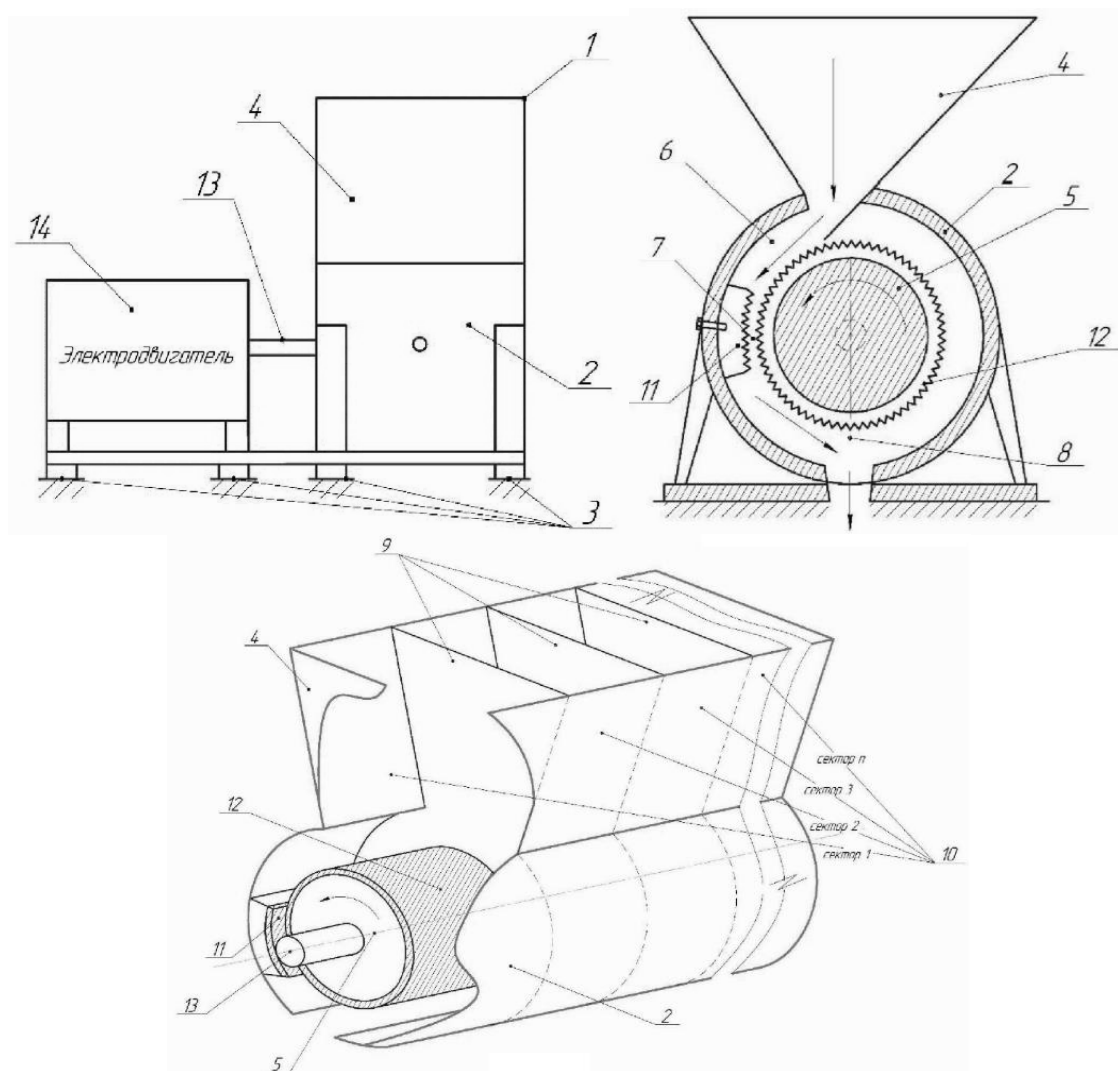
Измельчитель по пат. РФ № 2829351: 1 – измельчитель; 2 – корпус; 3 – амортизирующие прокладки; 4 – загрузочный бункер; 5 – ротор; 6 – загрузочная камера; 7 – дробильная камера; 8 – разгрузочная камера; 9 – перегородки; 10 – сектора; 11 – рифленные поверхности статора; 12 – поверхности ротора; 13 – привод; 14 – электродвигатель
